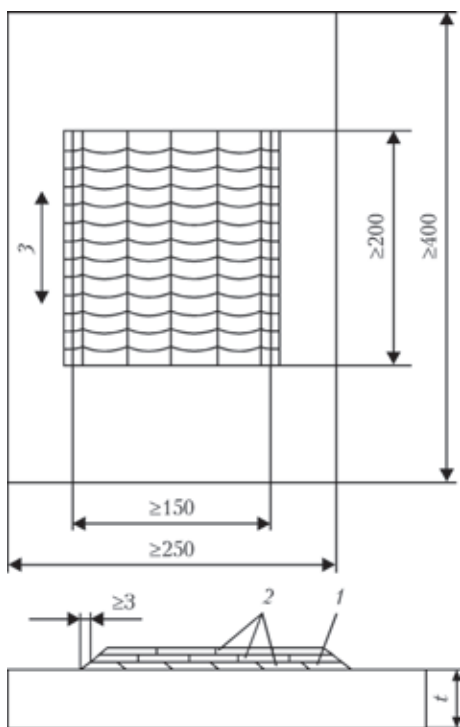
Наплавленный контрольный образец (пластина): 1 — буферный слой (подслой, наплавляется по необходимости); 2 — номера слоев согласно pWPS или общая толщина наплавленного слоя; 3 — направление наплавки; *t* — толщина основного металла [1]
